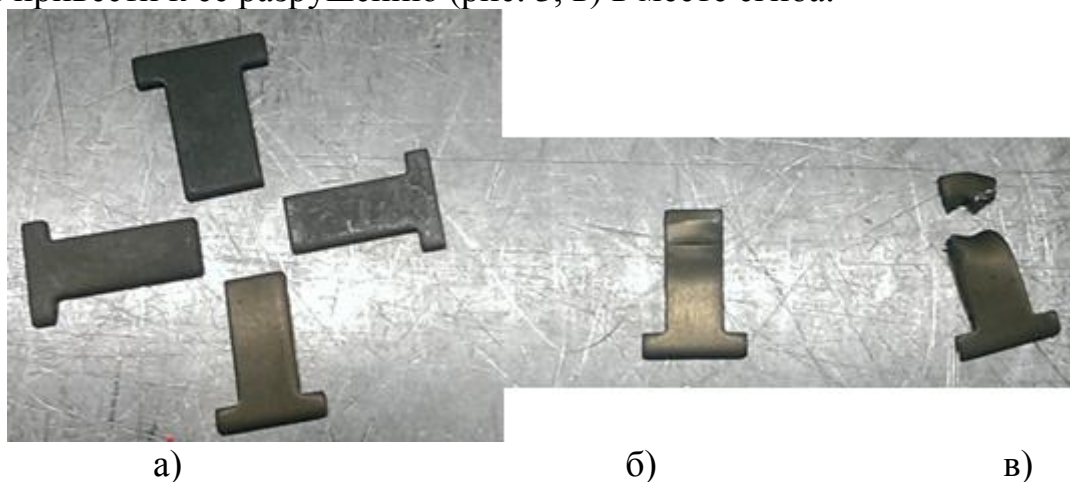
Контровочные пластины ТНД: а - контровочные пластины разных типов; б - использованная контровочная пластина; в - контровочная пластина после срыва гайки
